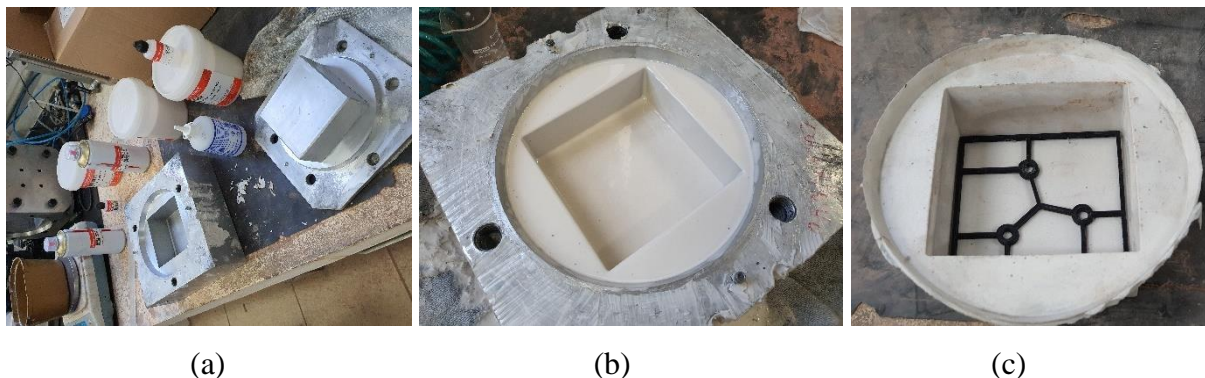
Moldagem *cushions* a) Molde e reagentes b) Preenchimento do molde c) Fixação dos imãs
